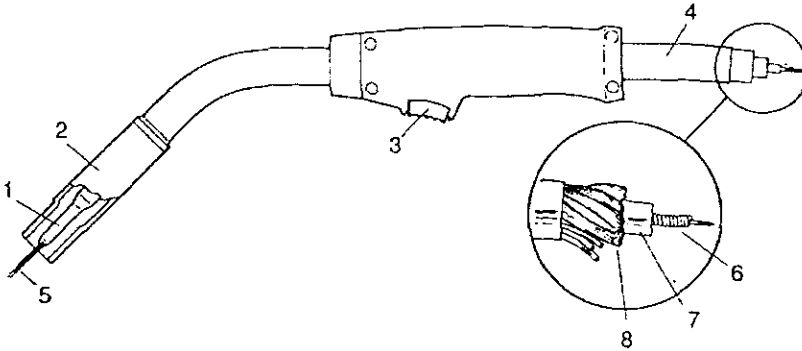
Pistola de soldar con paquete de manguera. 1.- Boquilla de contacto, 2- Tobera para gas de protección, 3.- Microinterruptor, 4.- Manguera, 5.- Alambre, 6.- Funda guía de alambre, 7.- Manguera para gas de protección, 8.- Cable de corriente.
